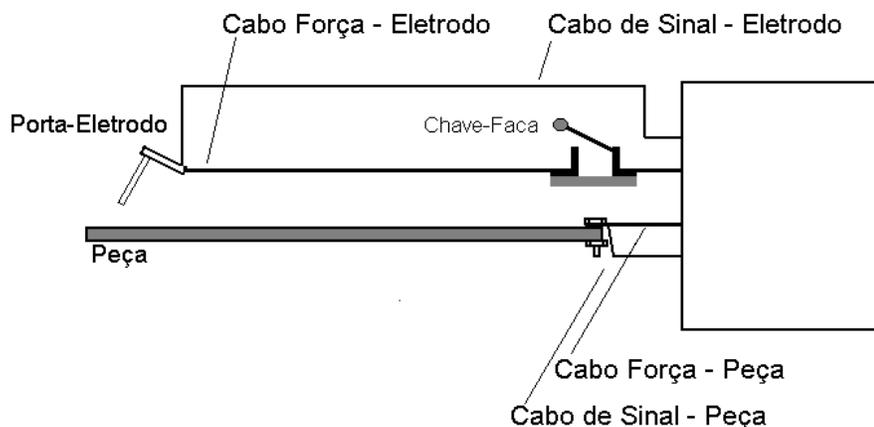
Configuração da ligação dos cabos de força e de sinal para a operação com a fonte HIPER-1 através da estrutura soldada.
